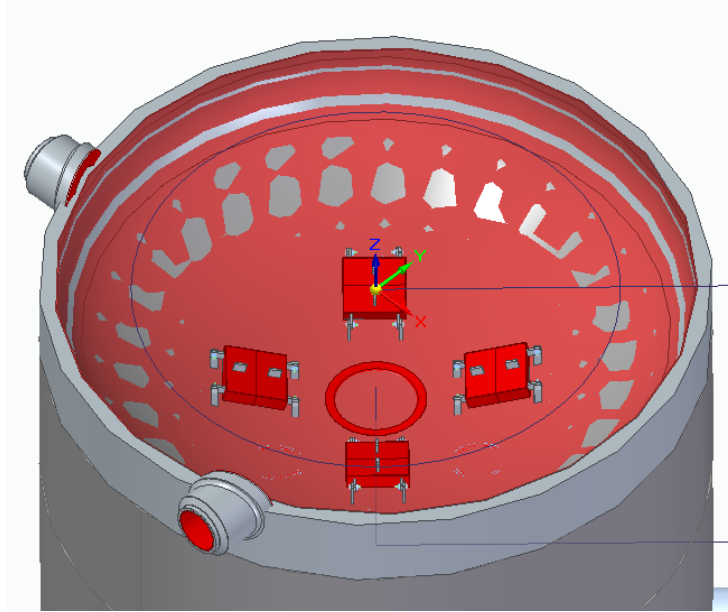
Modelo 3D de internos soldados a equipo
